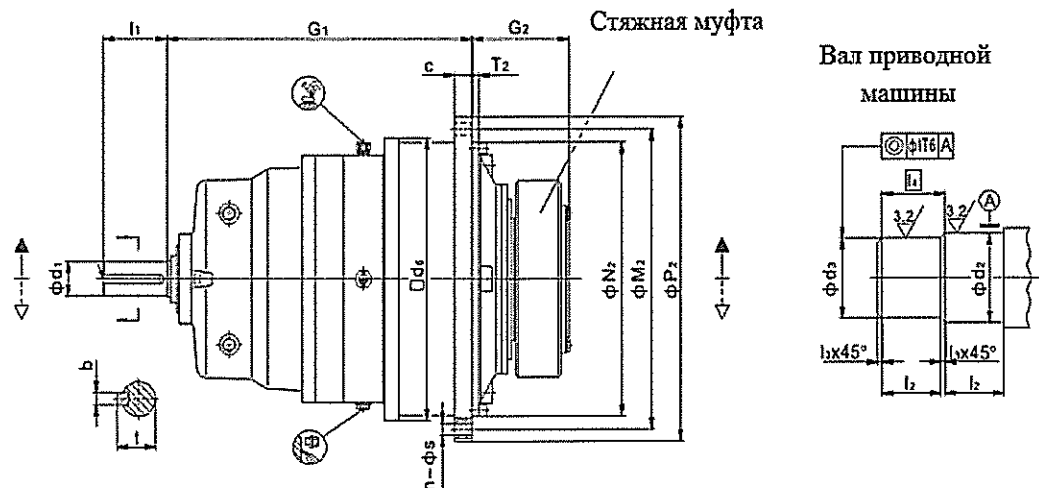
Редуктор планетарный 6П2 (габарит 31)
